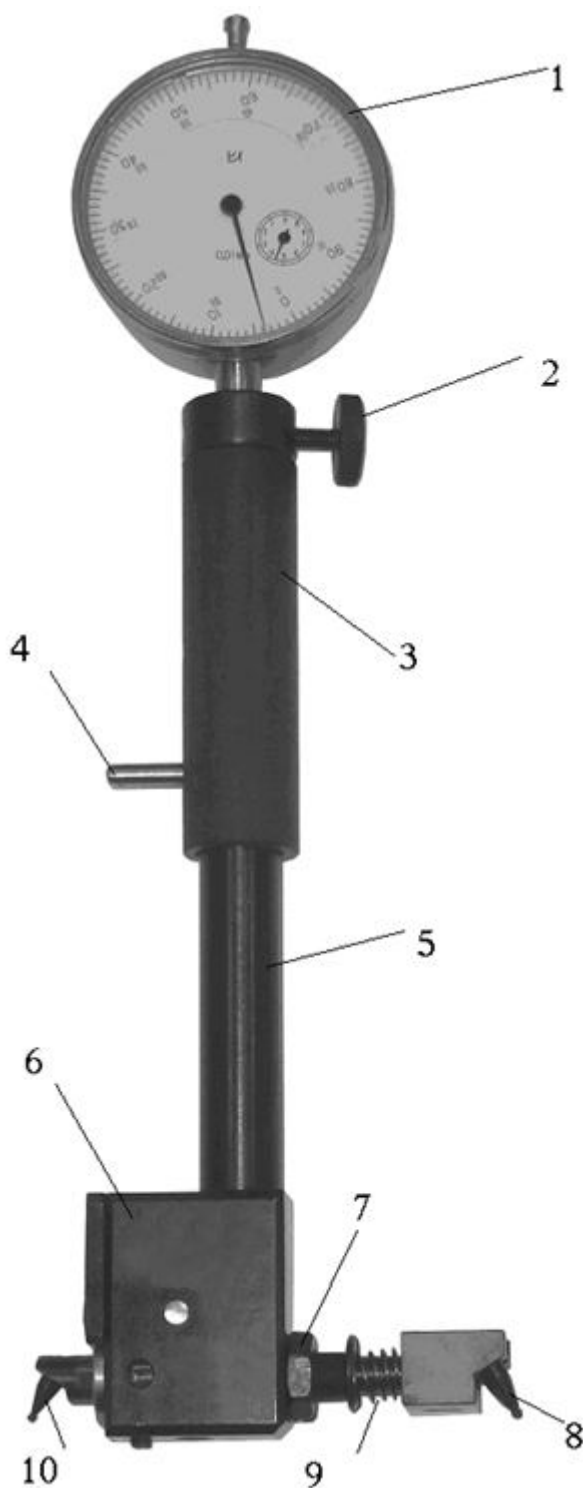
Типовая конструкция индикаторного прибора для измерения диаметра уплотнительной расточки муфты в области упорного уступа:
